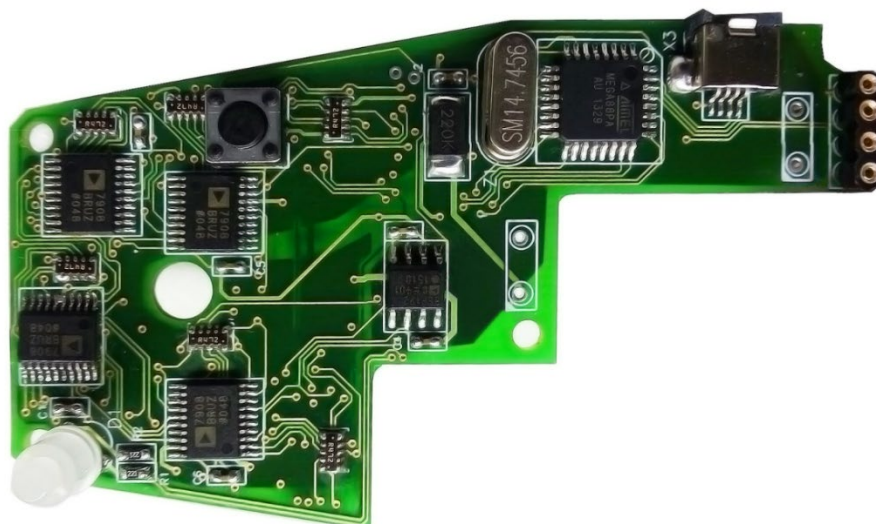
Печатная плата прибора автоматизированного контроля (вид сверху).
